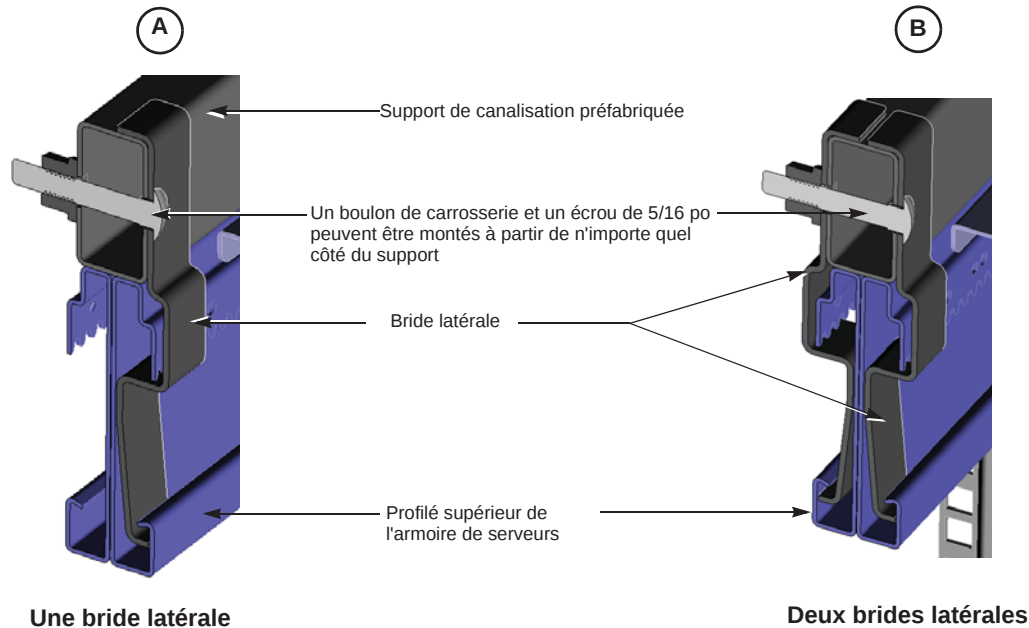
Bride d'extrémité du support fixée au toit d'une armoire SX de 600 mm (23,6 pieds)
